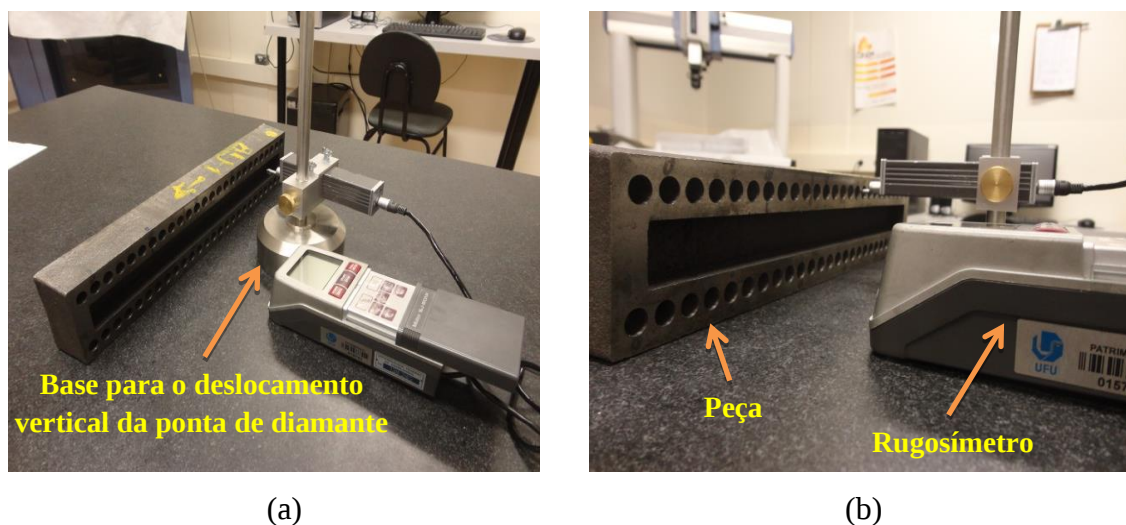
a) Montagem do equipamento para medição da rugosidade; b) Medição da rugosidade do furo a 180° um do outro em relação ao diâmetro do furo.
